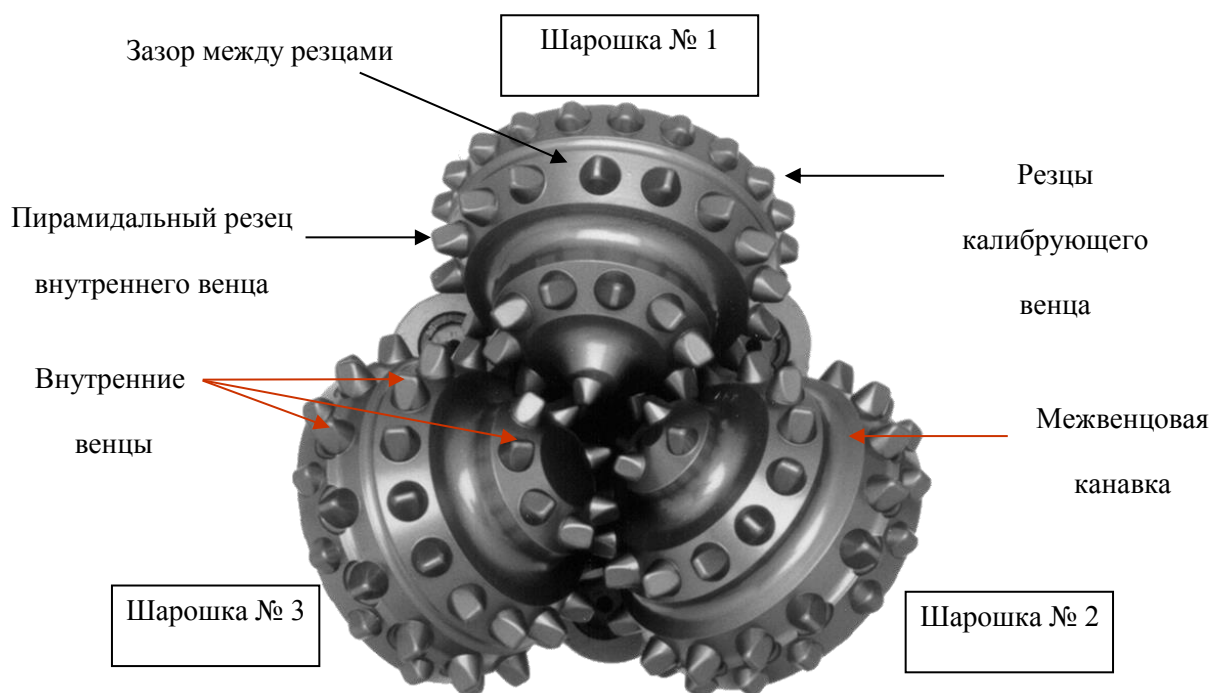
Номенклатура деталей долота с твердосплавными вставками
